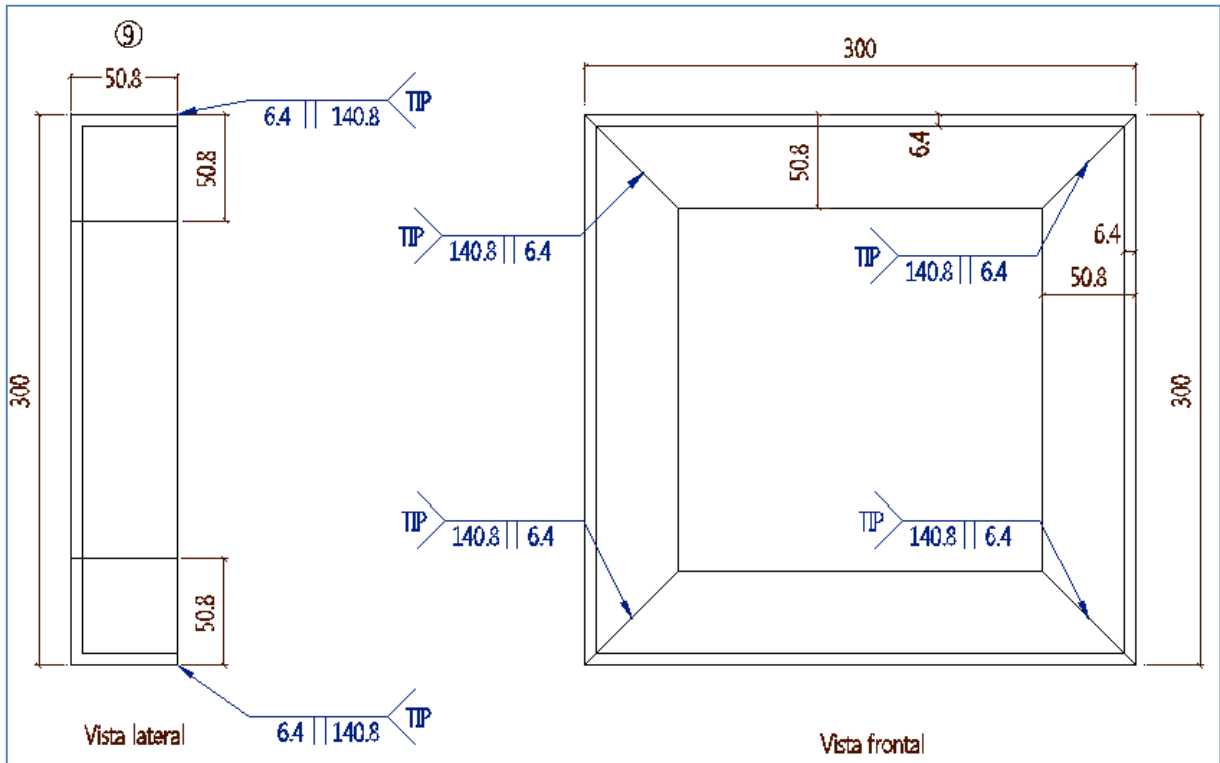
Detalle despiece pieza No.9 modelo 2 tensión.
